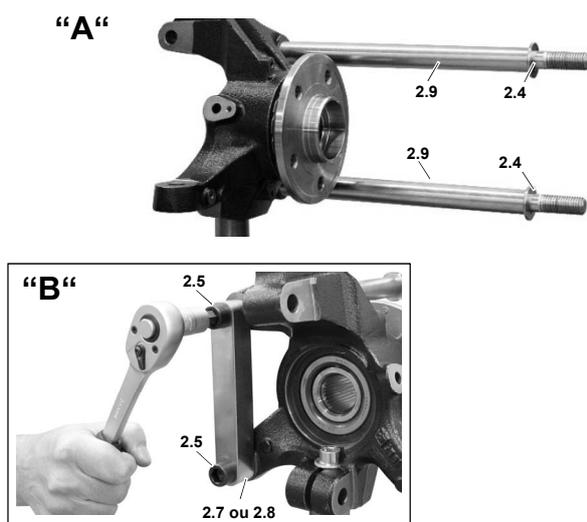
Monter la plaque de base sur les barres d'appui.
